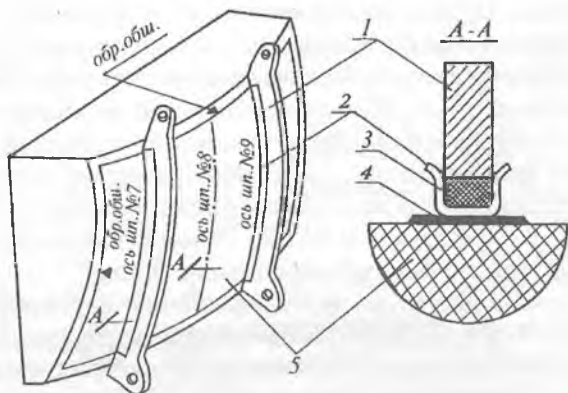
Получение рабочего контура рубильника методом слепка: 1 — рубильник; 2 — лента; 3 — слепок с поверхности макета; 4 — технический вазелин; 5 — макет поверхности
